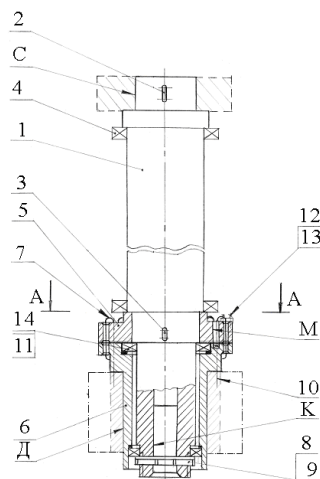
Верстатний шпиндель з гасінням віброколивань
